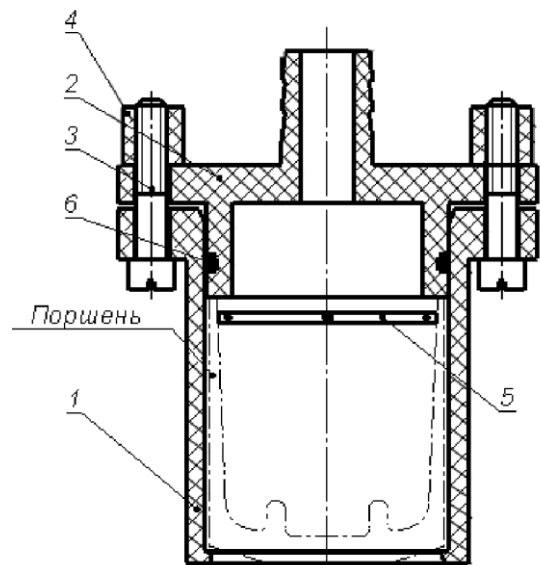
Пристосування для обробки головки поршнів: 1 – корпус; 2 – кришка; 3 – гвинт; 4 – гайка; 5 - струмопідвідне кільце; 6 - кільце ущільнювальне
